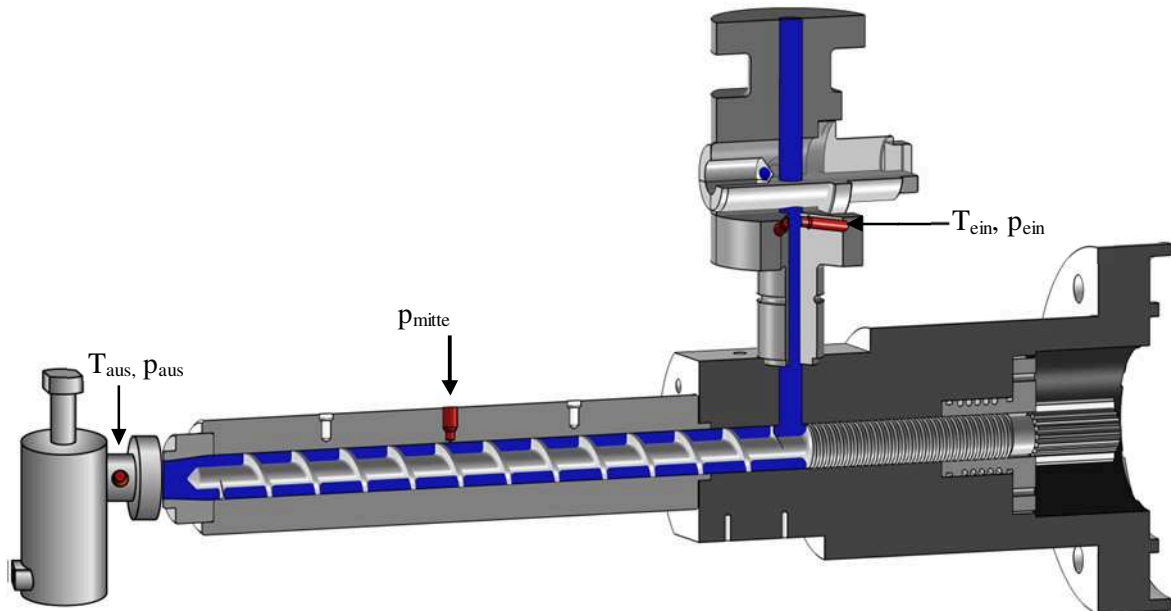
High-Speed-Extruder mit Bypass-Modul und Druckdrosselwerkzeug
